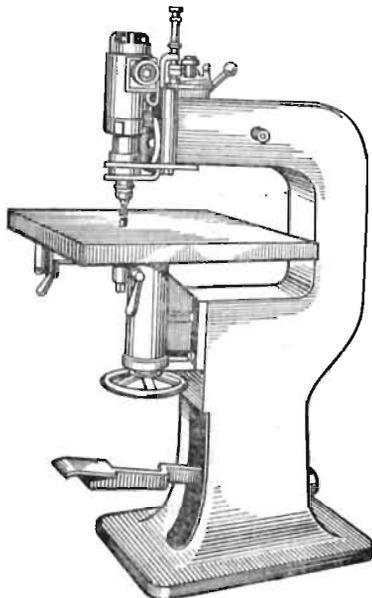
Вертикально-фрезерный станок с верхним расположением шпинделя и нижним расположением копирного пальца
